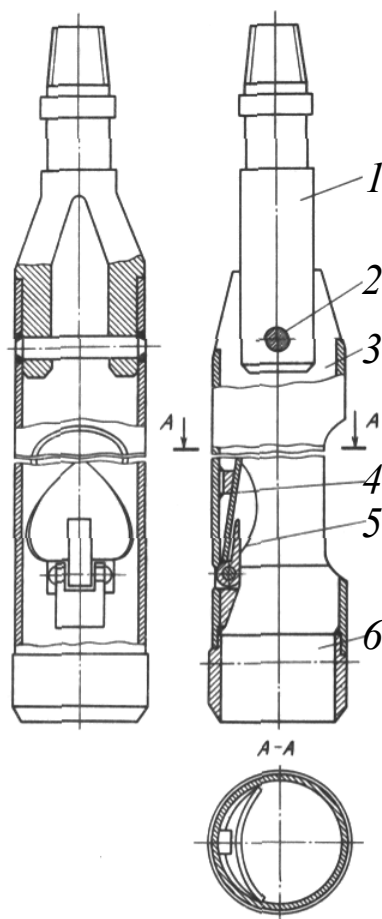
Устройство виброндзы с клапаном: 1 – переходник; 2 – палец; 3 – корпус; 4 – упор; 5 – клапан; 6 – рабочее кольцо
